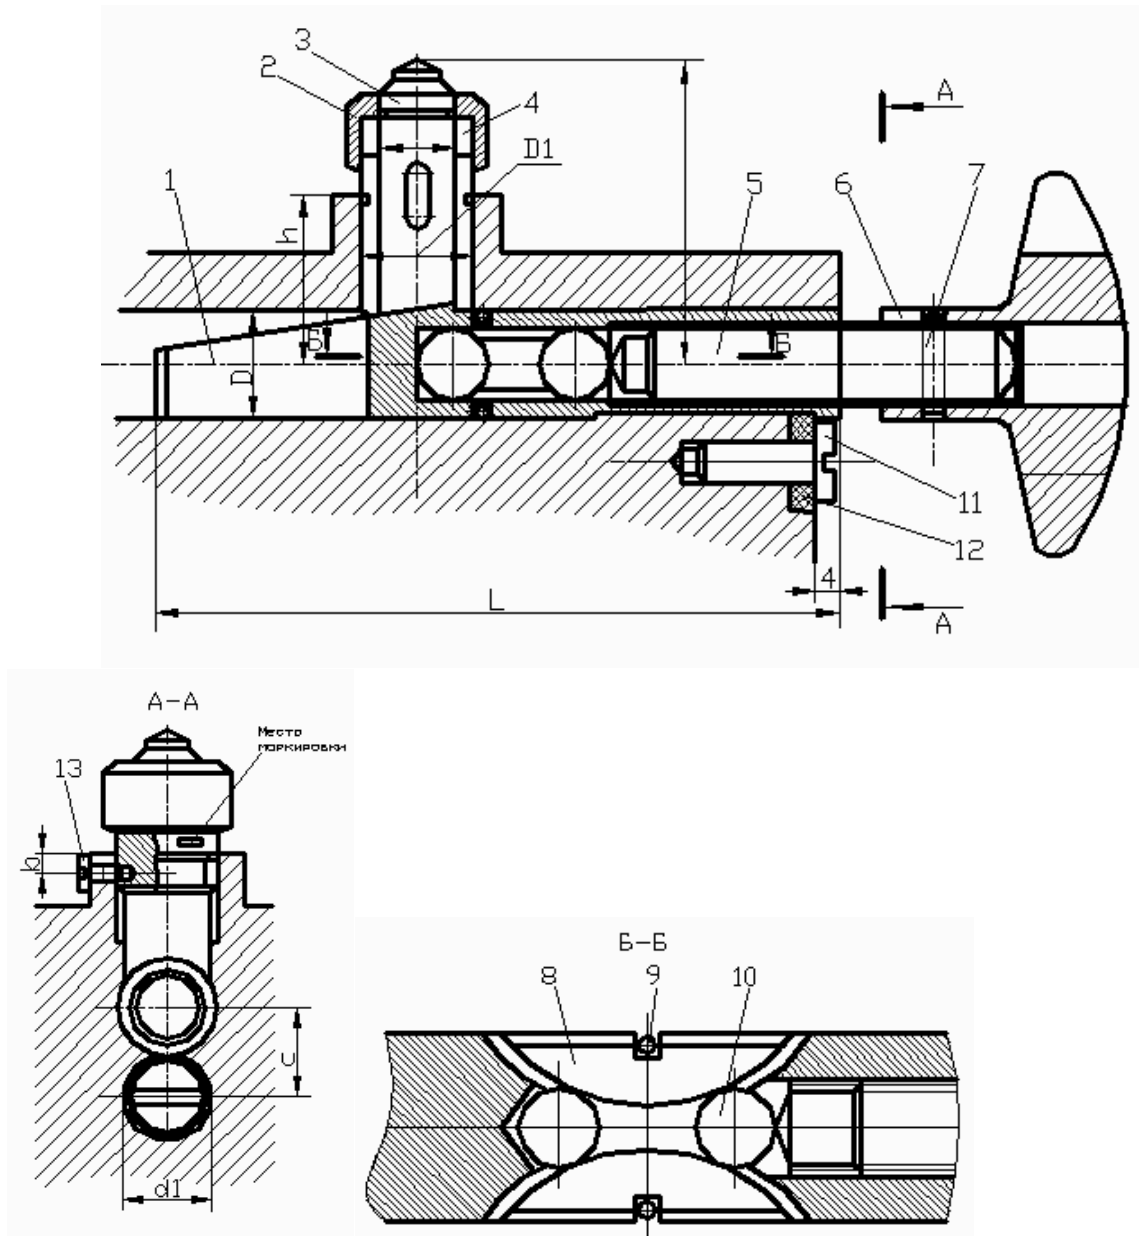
Подводимая клиновидная вспомогательная опора: 1 – клин; 2 – колпачок; 3 – опорный штырь; 4 – втулка; 5 – нажимной винт; 6 – звездообразная рукоятка; 7 – штифт; 8 – кулачок; 9 – замковое кольцо; 10 – шарик; 11, 12, 13 – винты и шайбы.
